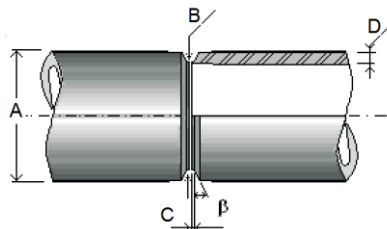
Desenho do tubo preparado para os ensaios de soldagem.
